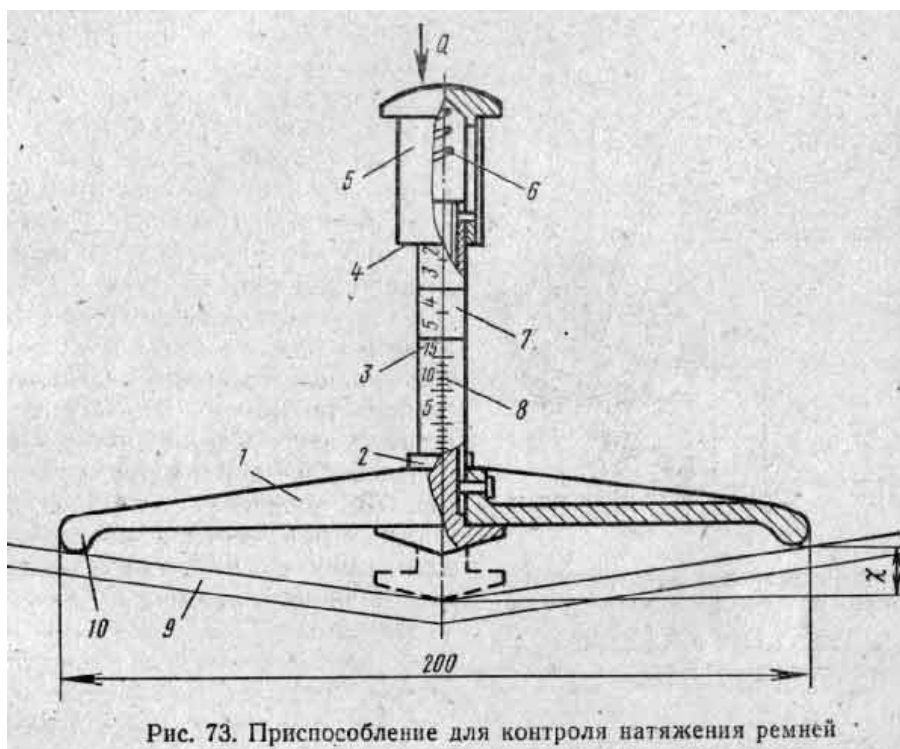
Приспособление для контроля натяжения ремней
